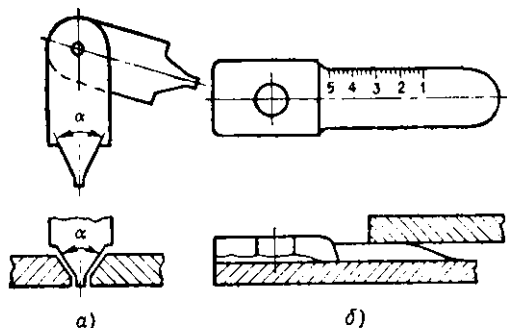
Шаблоны для проверки сборки сварных соединений:
